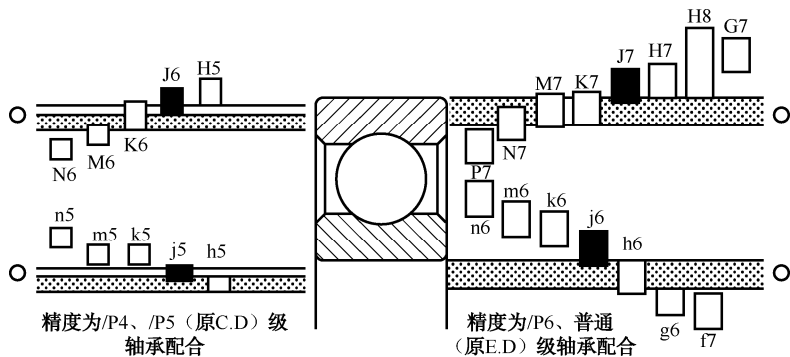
轴承内圈与回转轴、轴承与不动外圈的配合
